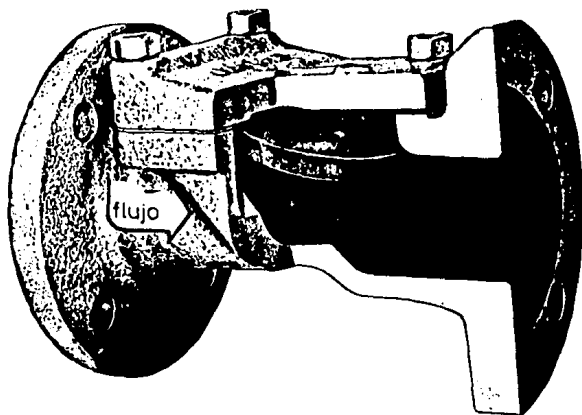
Válvula Check Oscilante con Clapeta de Goma
